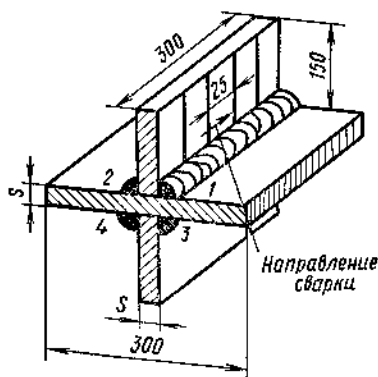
Крестовая проба (1 — 4 — порядок сварки швов)
